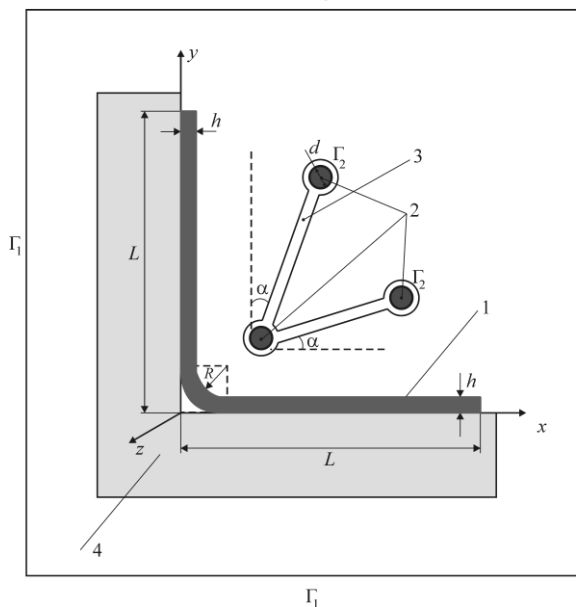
Розрахункова схема вигнутої заготовки разом із двовитковим індуктором та діелектричною матрицею: 1 – заготовка; 2 – витки струмопроводу індуктора; 3 – ізоляція індуктора; 4 – діелектрична матриця
